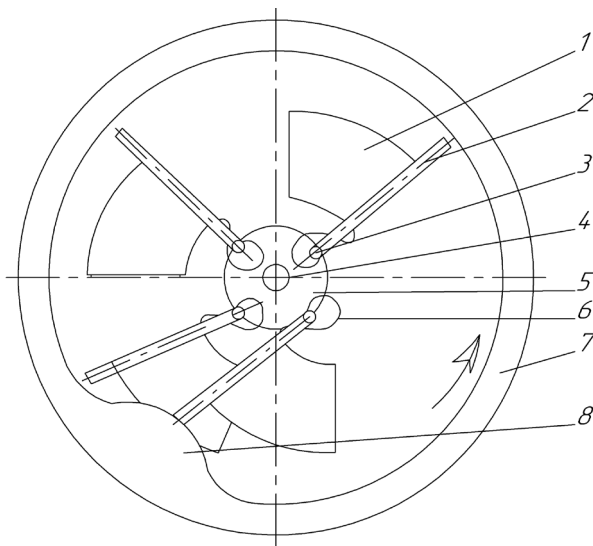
Схема відцентрового робочого органу із регульованим рухом лопаток: 1 – лопатка; 2 – палець; 3 – вісь лопатки; 4 – привідний вал; 5 – маточина; 6 – спіральна пружина; 7 – профільна шайба; 8 – випуклість шайби.
